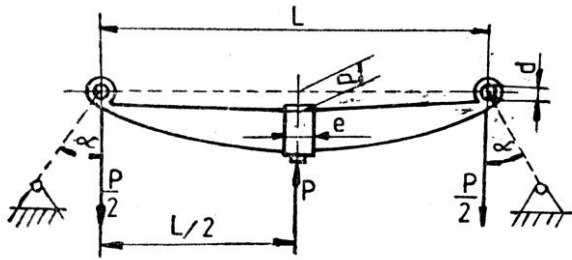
Arc trapezoidal suspendat la capete prin inele înclinate
